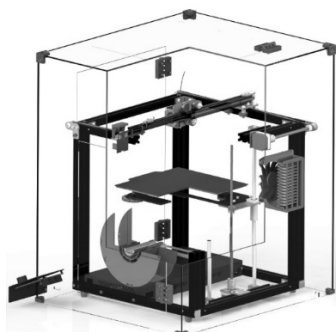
Конструкция кожуха 3D-принтера с системой фильтрации воздуха
